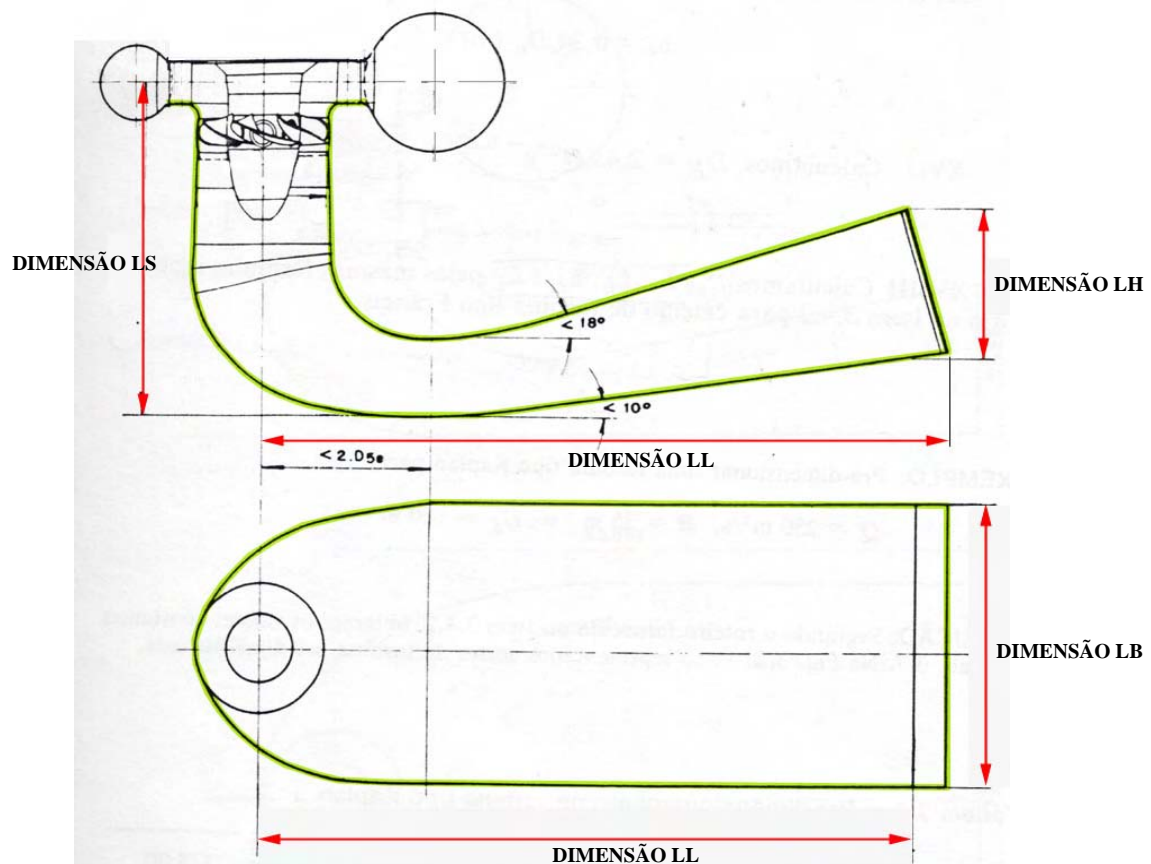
Dimensões do Tubo de Sucção da Turbina Kaplan
